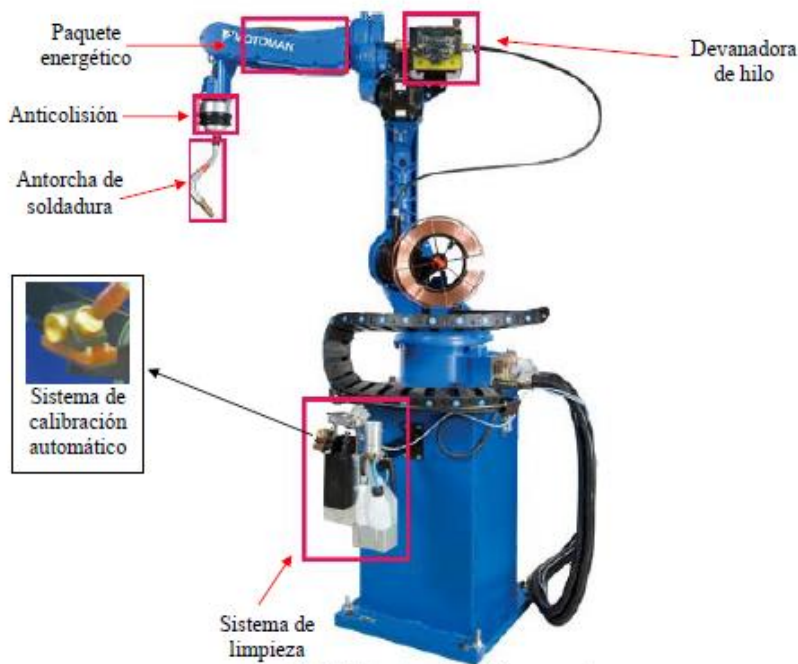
Partes de un robot motoman de soldadura (Coca García J, P. 29).
